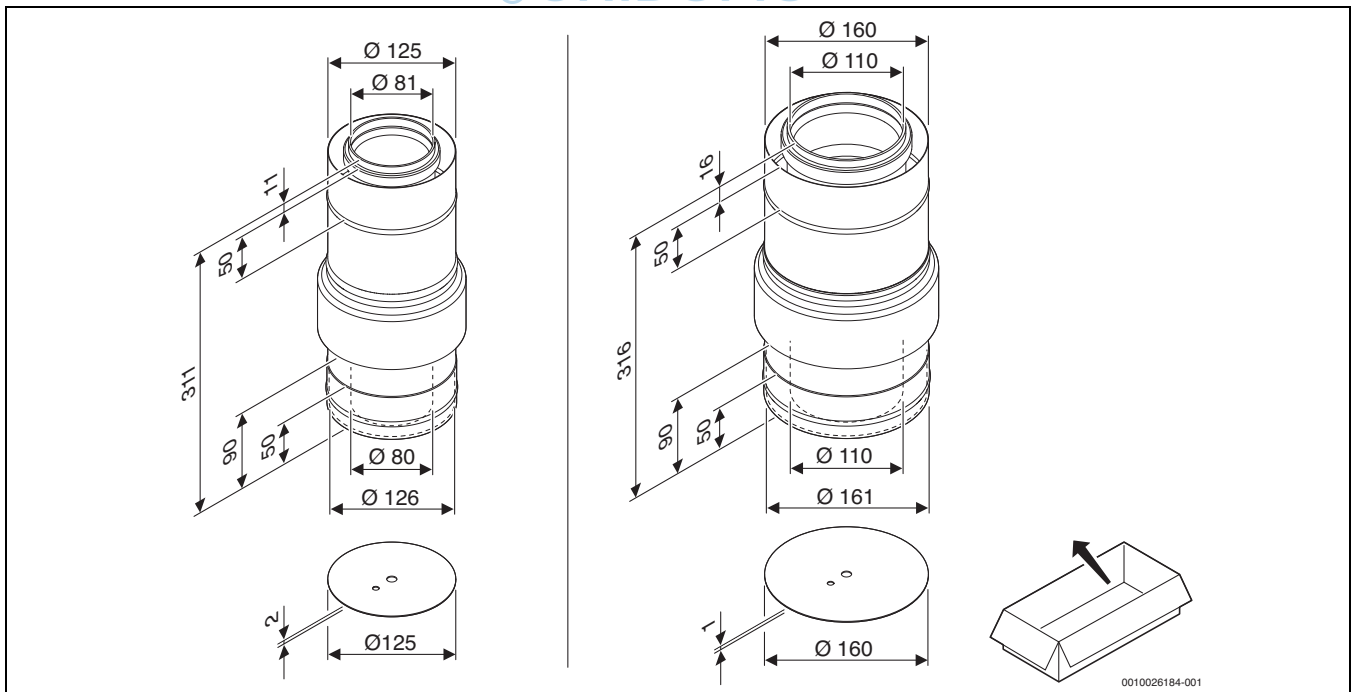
Ø 80/125 mm: 7738112705, Ø 110/160 mm: 7738113147
